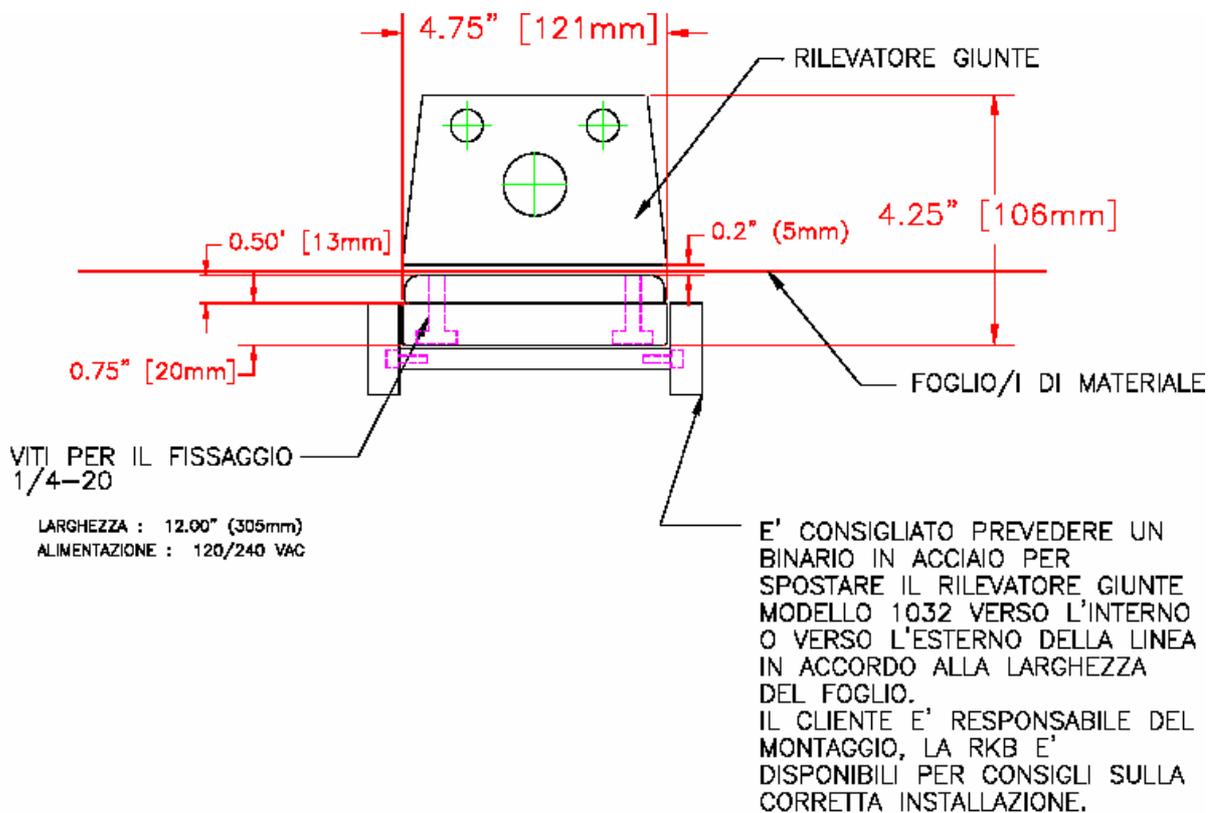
Dimensioni installazione trasversale Rilevatore Giunte
